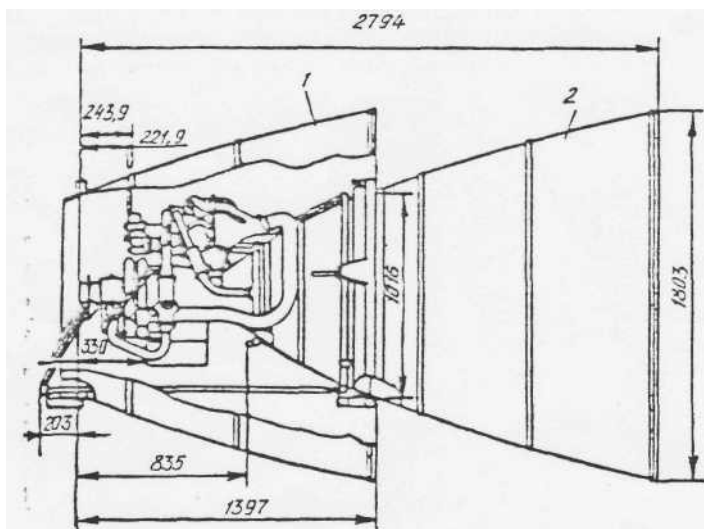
Модифицированный двигатель RL-10 с раздвижным соплом: 1 - транспортное положение; 2 - рабочее положение
